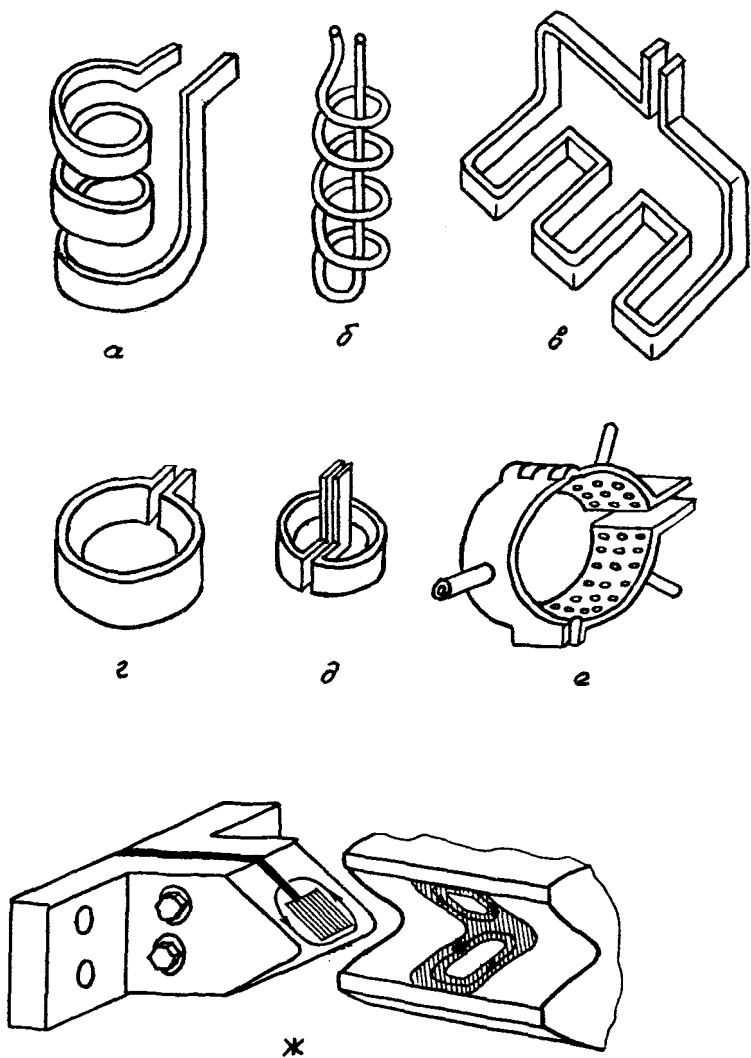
Схемы индукторов для нагрева ПВХ: а, г — наружных цилиндрических поверхностей; б, д — внутренних цилиндрических поверхностей; в — плит и плоскостей методом перемещения; е — шеек коленчатых валов; ж — крупно-
